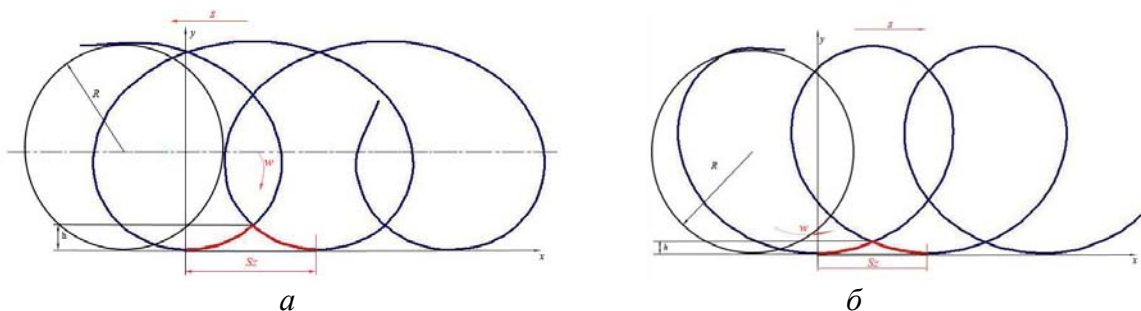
Траектория режущей кромки фрезы при попутном (а) и встречном (б) фрезеровании
